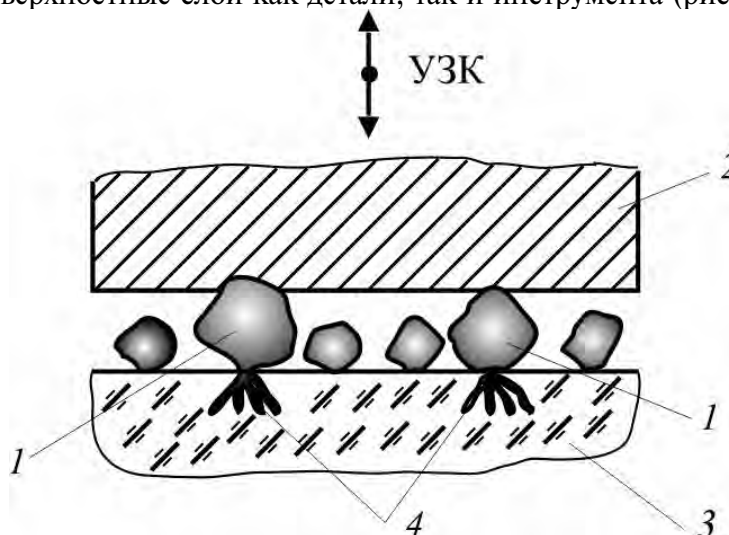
Схема взаимодействия абразивных зерен с поверхностью заготовки и инструмента в процессе ультразвуковой размерной обработки:
